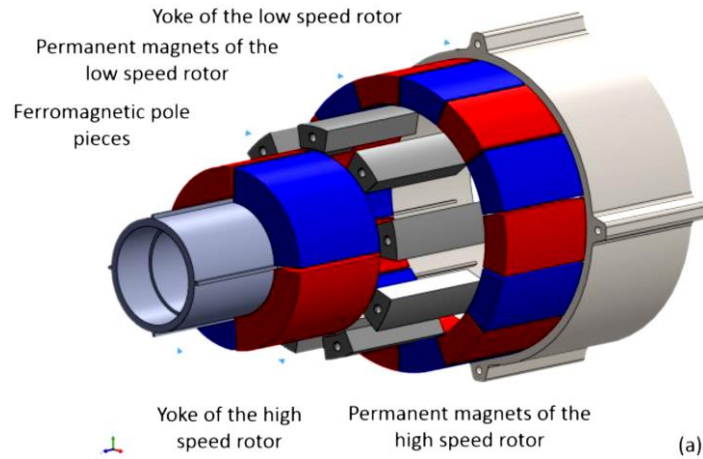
Vue éclatée de l'engrenage magnétique [DES16].
